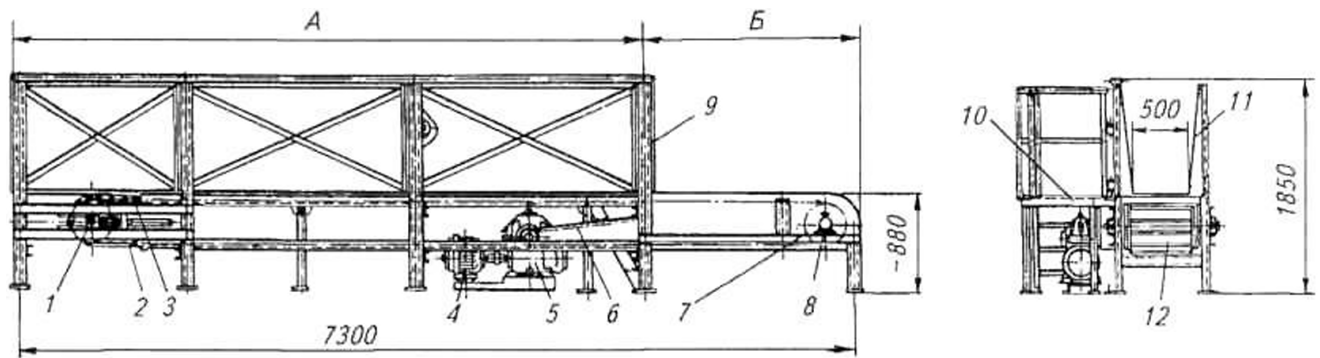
Пластинчатий конвеєр для глушення свиней:
